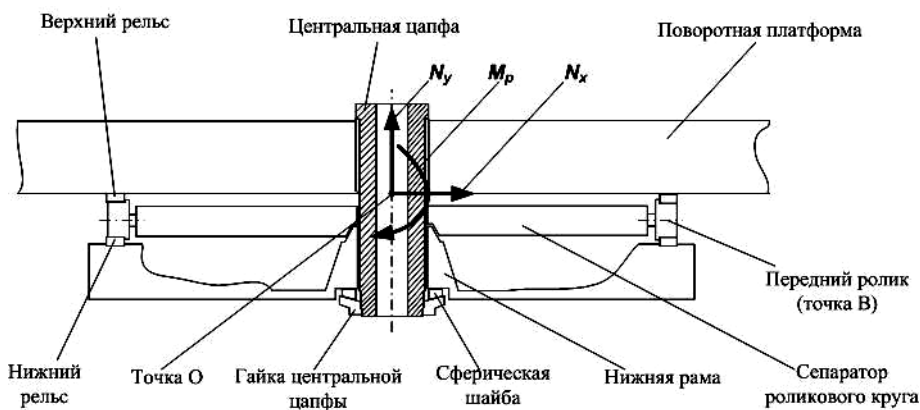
Схема общей конструкции опорно-поворотного устройства и расположения реакций связей
